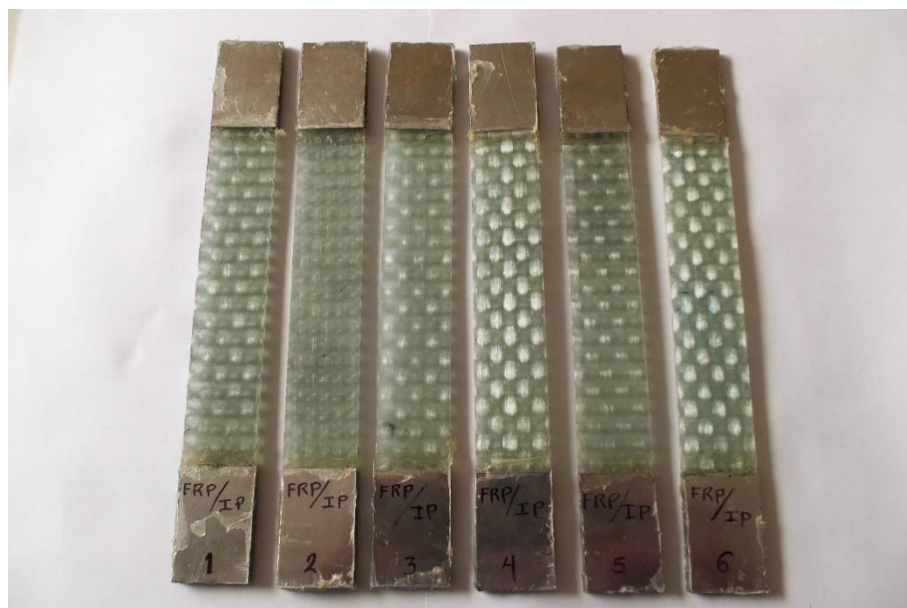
Probetas de tensión manufacturadas por infusión-presión.
